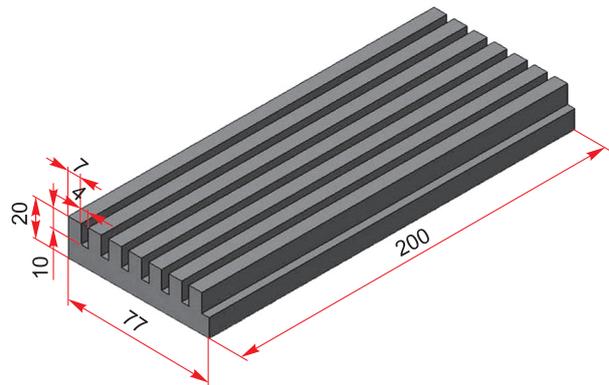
Внешний вид заготовки из стали 12Х18Н10Т
